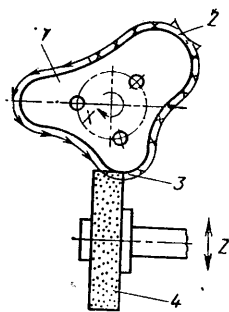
Схема работы установки «Работат»: 1 — отливка (вращается относительно оси X); 2 — приближающаяся часть отливки; 3 — зачищаемая поверхность; 4 — шлифовальный круг
